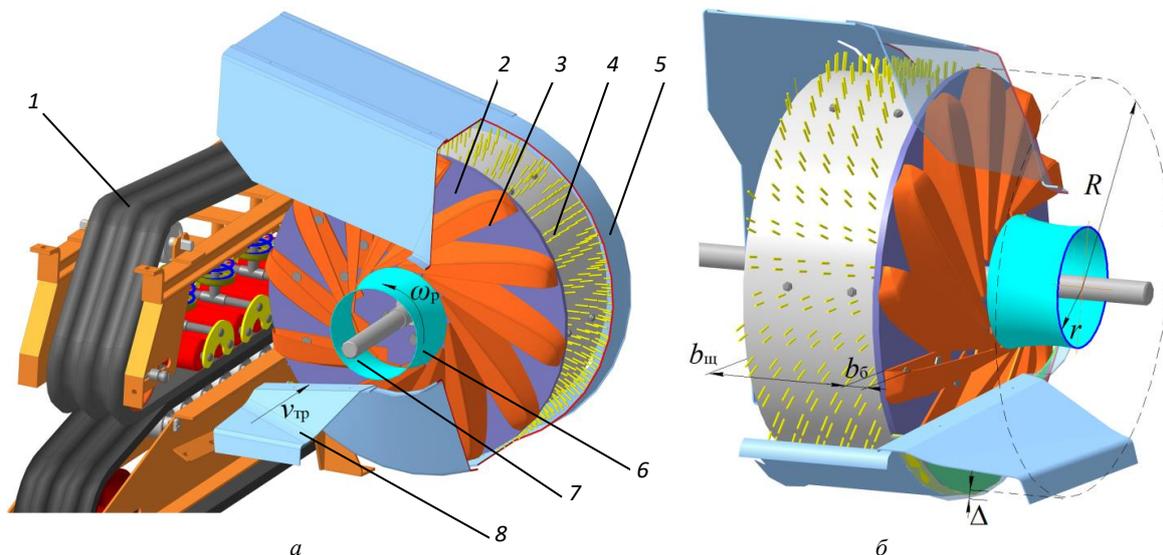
Конструкция роторного бильно-вычесывающего устройства: *a* – общий вид устройства; *б* – общий вид ротора; 1 – жазимной транспортер; 2 – ротор; 3 – бичи; 4 – вычесывающе-транспортирующая щетка; 5 – кожух; 6 – кольцо; 7 – вал ротора; 8 – стол
